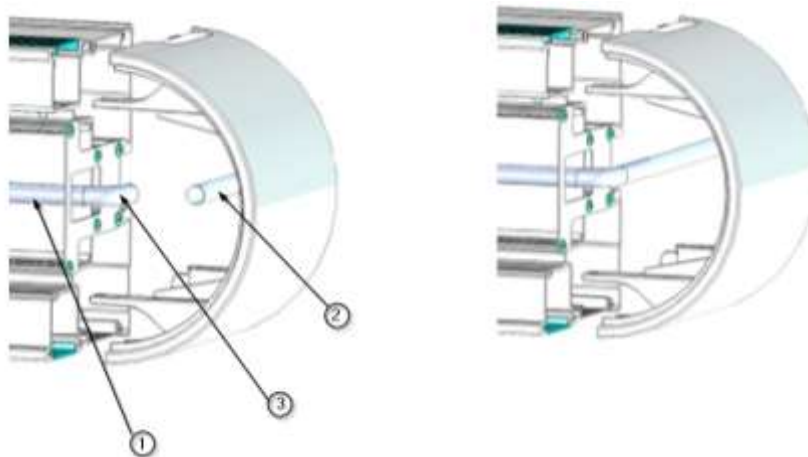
Tăierea tuburilor și montarea accesoriilor din cupru
